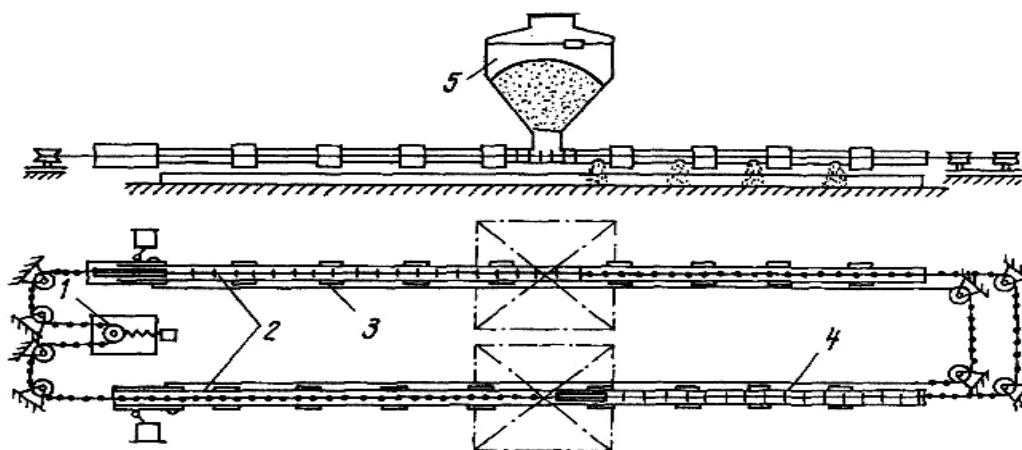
Схема штангово-шайбового кормораздатчика РКА-1000 (1 – приводная станция, 2 – кормопровод, 3 – дозатор, 4 – шайбовый транспортер, 5 – бункер).
